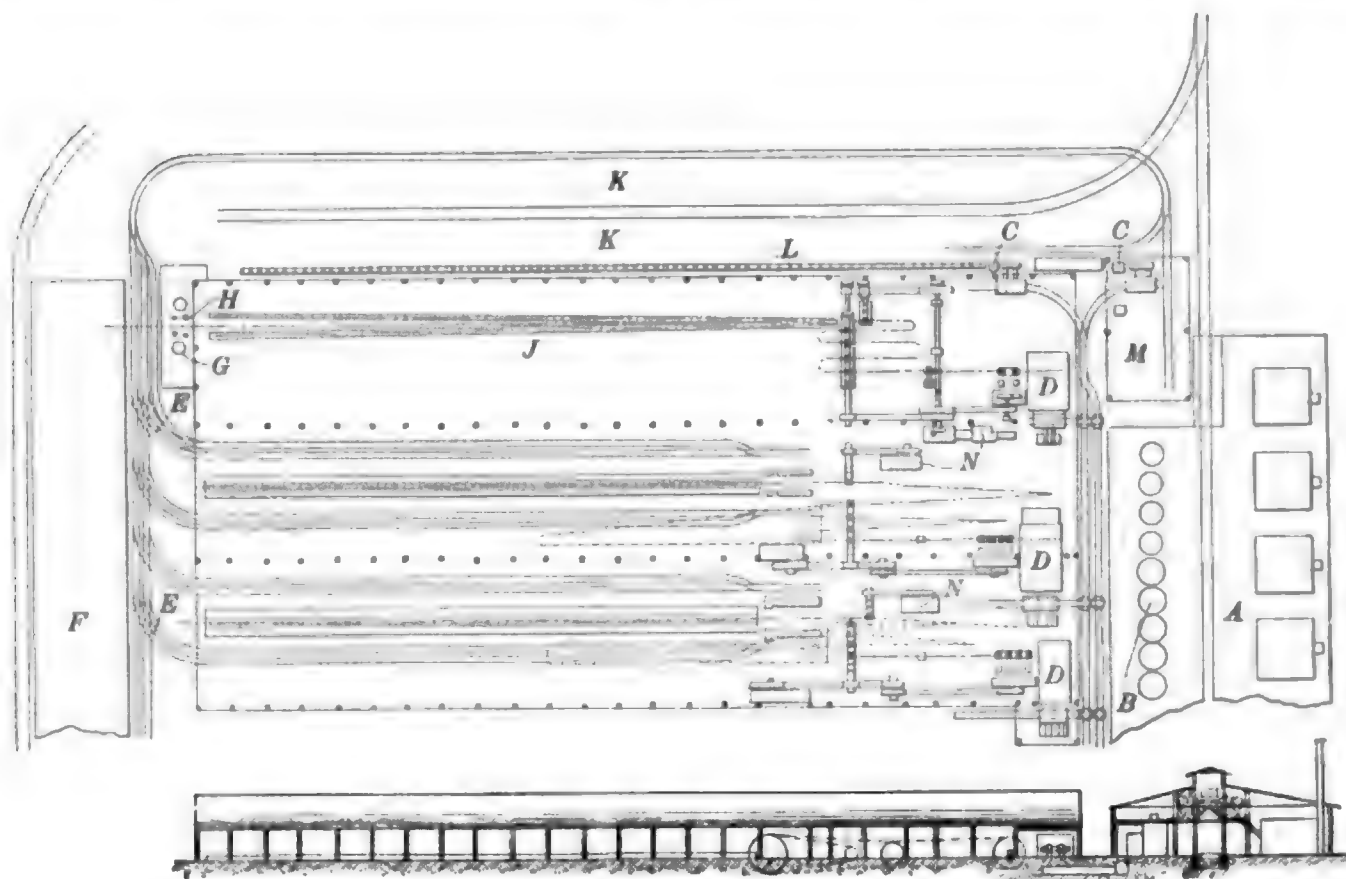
Plan eines Walzwerks für Band- und Handelseisen.
